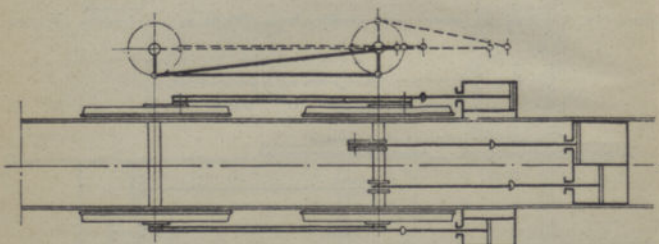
Mechanismo motor de locomotiva compound, de 4 cilindros.
